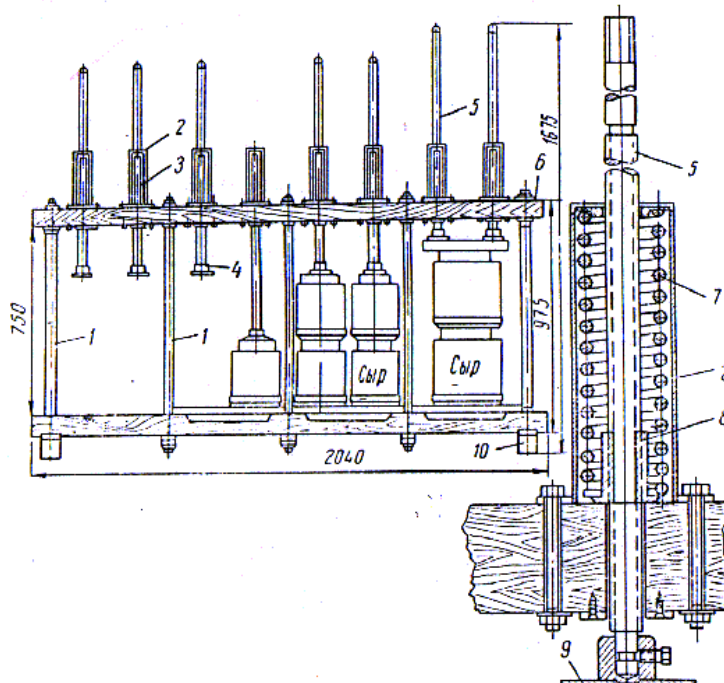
Вертикальний пружинно - гвинтовий прес.
